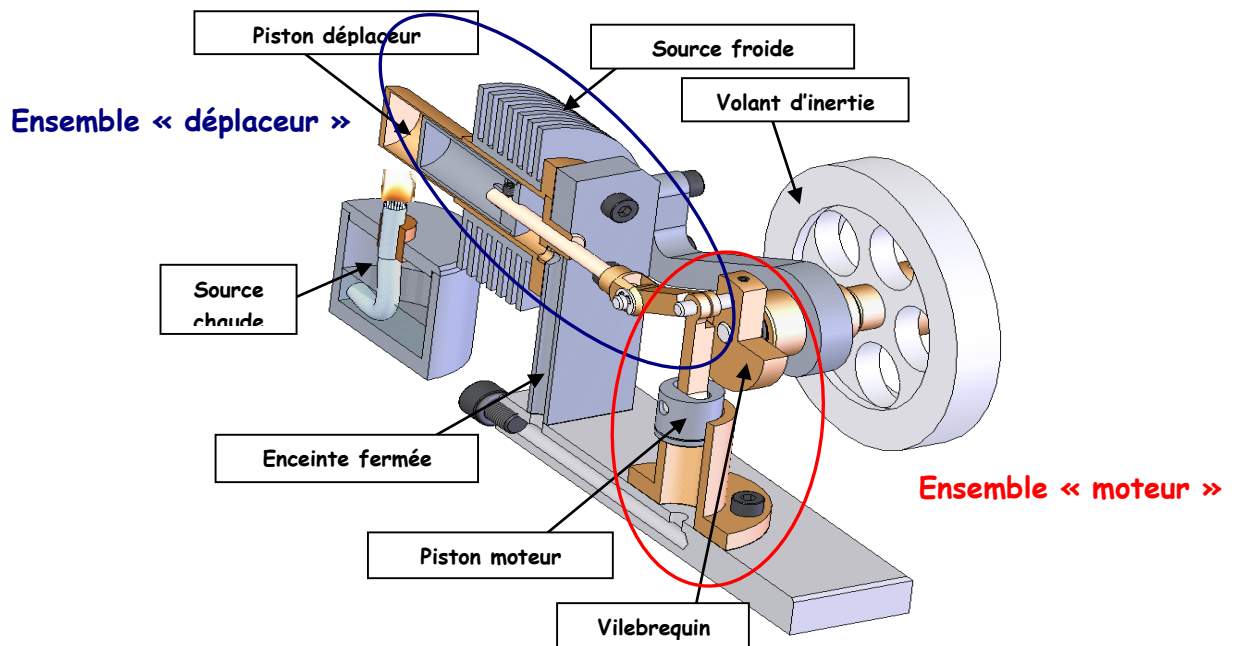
Moteur Stirling (Ensemble déplaceur-moteur).
